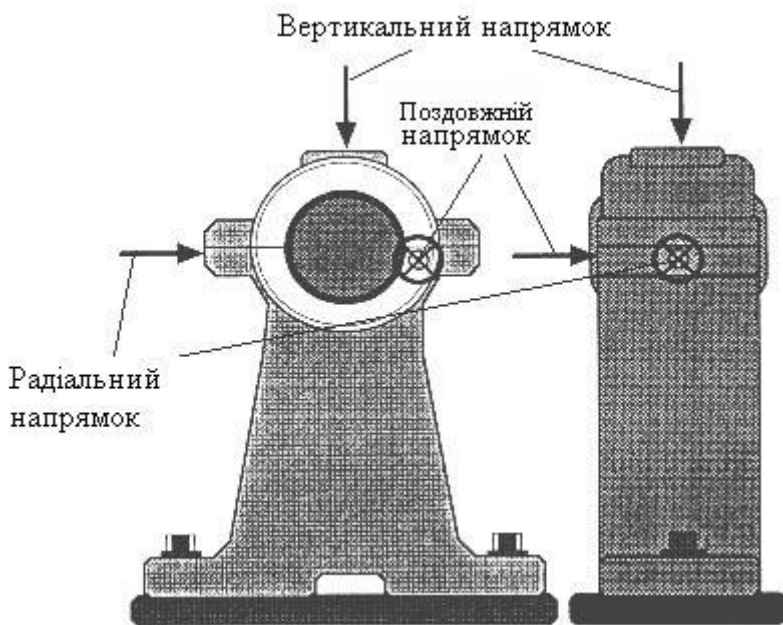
Контрольні точки вимірювань вібрації на корпусі підшипникових опор ротора
